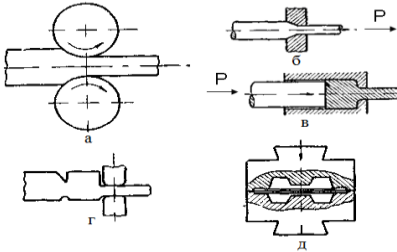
Схеми обробки заготовок тиском: а – прокатування; б – волочіння; в – пресування; г – кування; д – штампування
